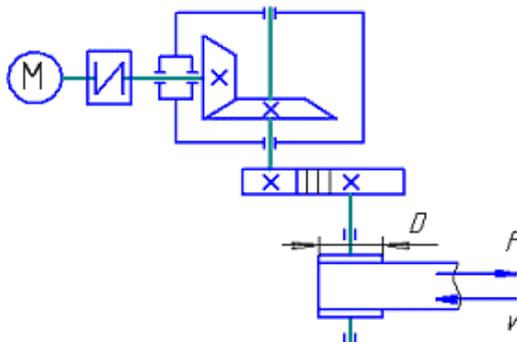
Кинематическая схема привода ленточного конвейера
